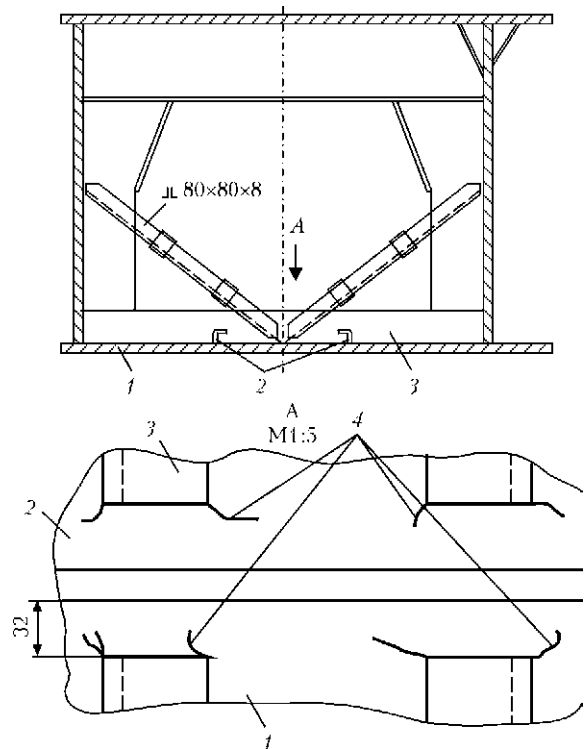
Схема нижнего сварного пояса пролетных балок перегружателя: 1 — нижний пояс пролетной балки перегружателя; 2 — диафрагма; 3 — уголки жесткости; 4 — трещины
